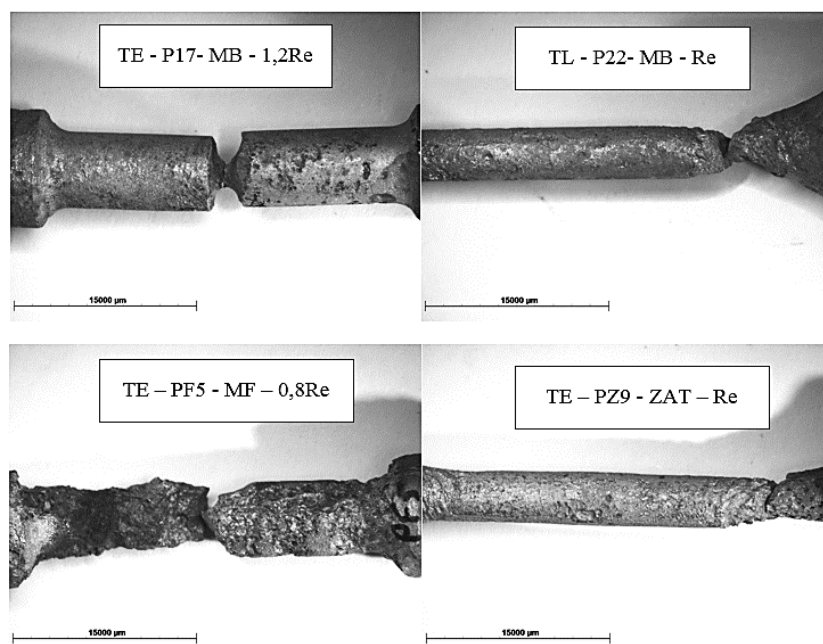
Macrographies des éprouvettes rompues en acier P285NH
